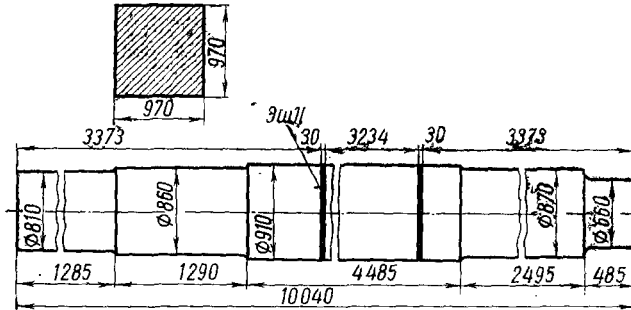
Сварной вал шахтной подъемной машины
